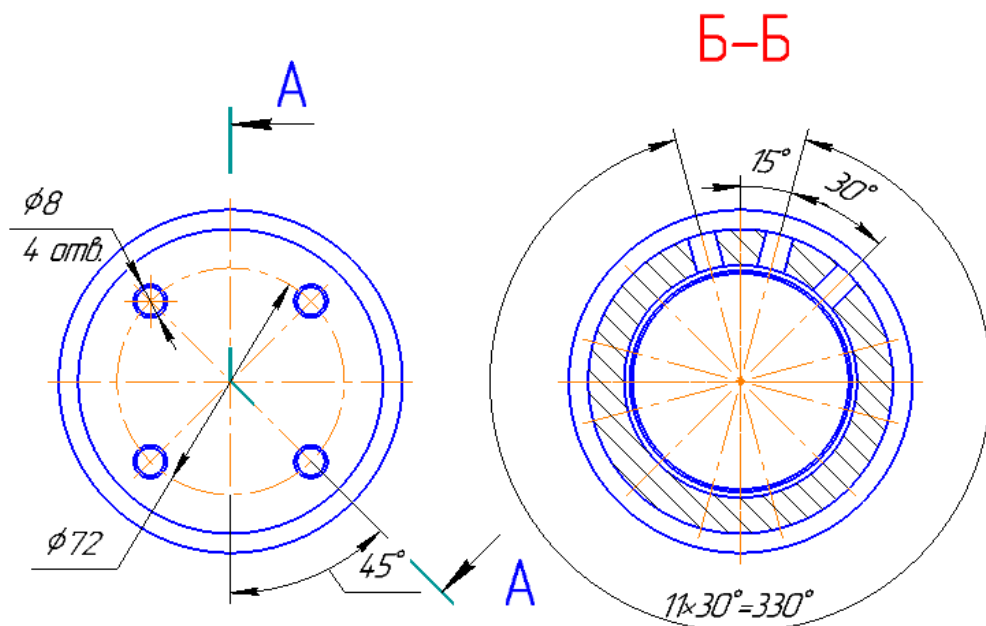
Ескіз заготовки. Сталь 45.
